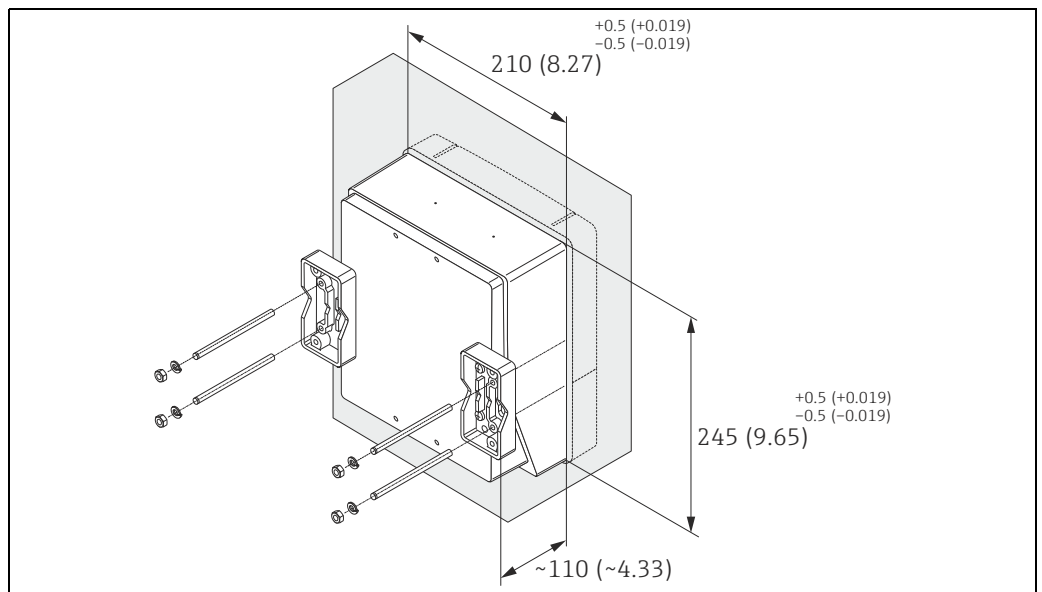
Schalttafeleinbau (Wandaufbaugehäuse)
